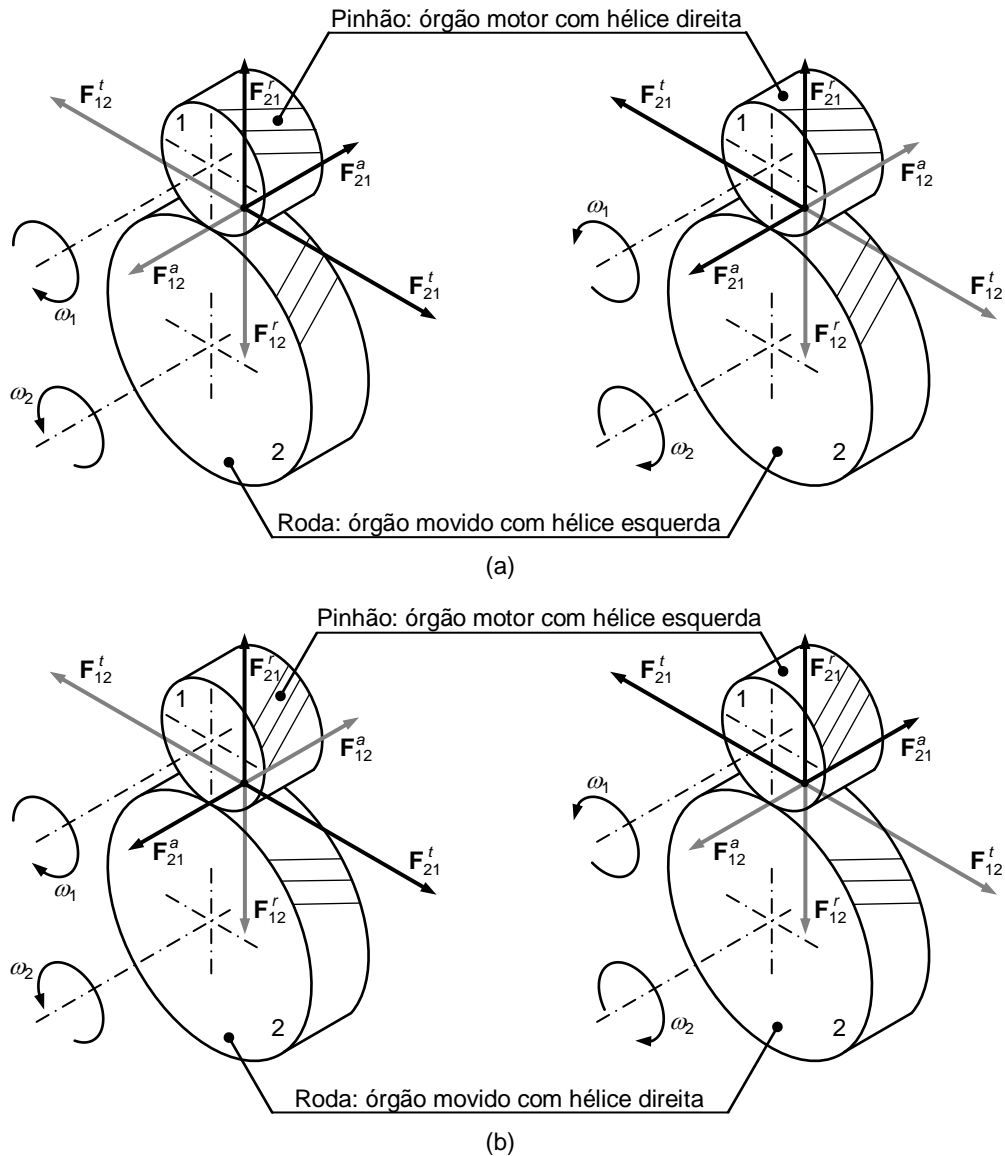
Força que se desenvolvem no pinhão e na roda em engrenagens cilíndricas de dentes inclinados: (a) O pinhão é o órgão motor com hélice direita e a roda com hélice esquerda; (b) O pinhão é o órgão motor com hélice esquerda e a roda com hélice direita.
